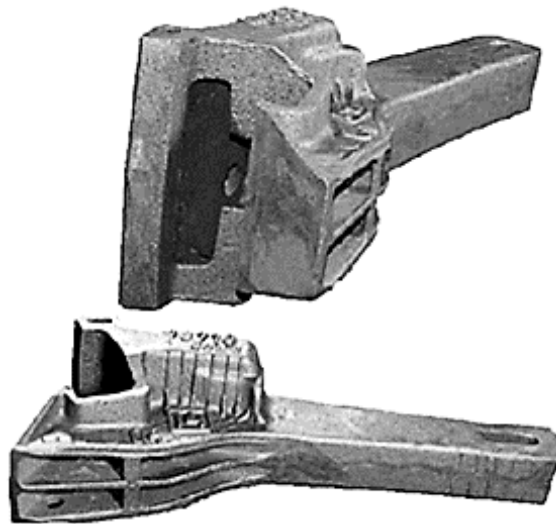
Загальний вигляд автозчепного пристрою СА-3
